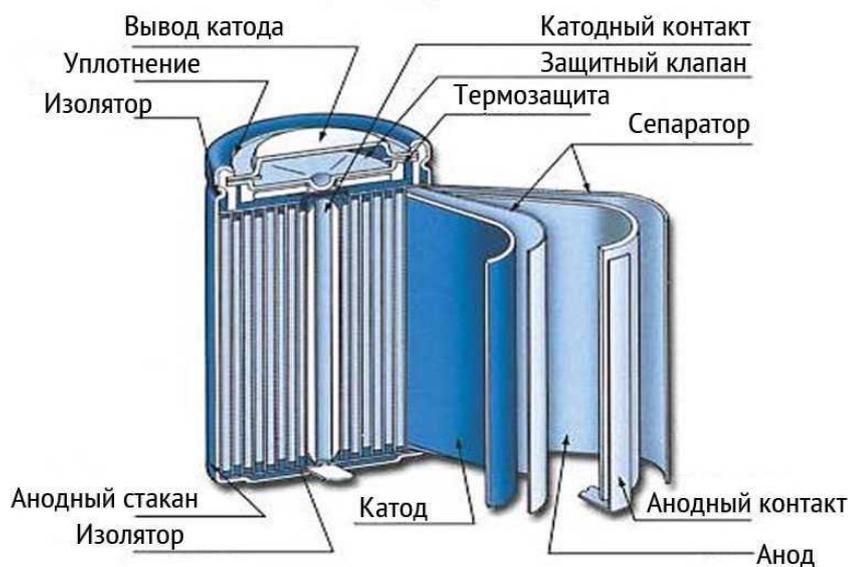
конструкция никель-металлогидридных аккумуляторов цилиндрической формы
